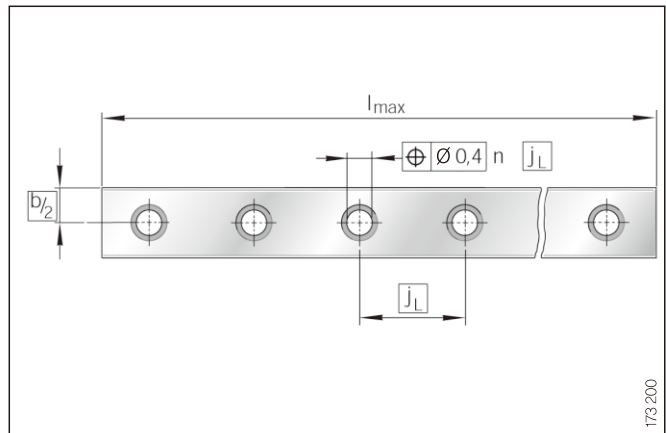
가이드웨이의 위치 및 길이 공차 - DIN ISO 1101에 의거하는 구멍 패턴
